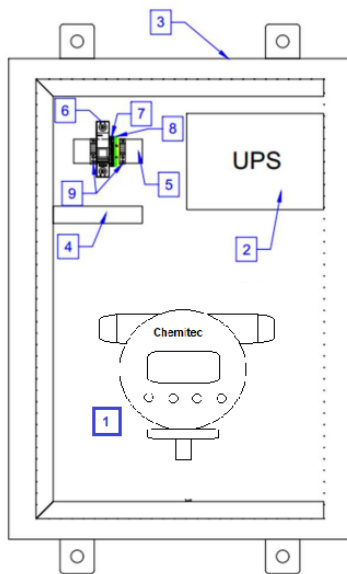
LUGAR DE INSTALACION MEDIDOR
